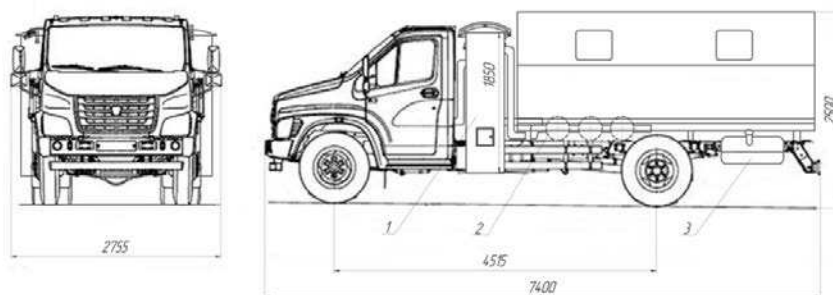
Компоновка мобильного комплекса на шасси Газон - Next: 1 – газогенераторы; 2 – батарея охладителей - очистителей; 3 – резервный топливный бак
